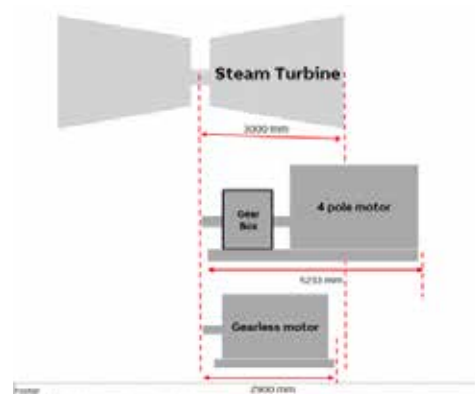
Rimpiazzo di turbine a Vapore mediante motori elettrici ad alta velocità (Gearless) a causa degli ingombri disponibili
